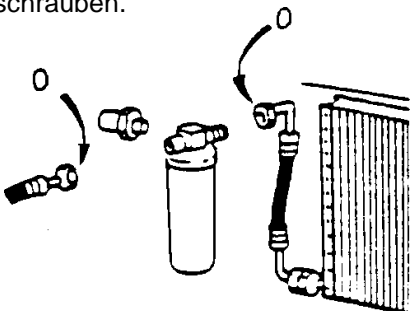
Austausch der alten R12 O-Ringe gegen neue R134a O-Ringe
